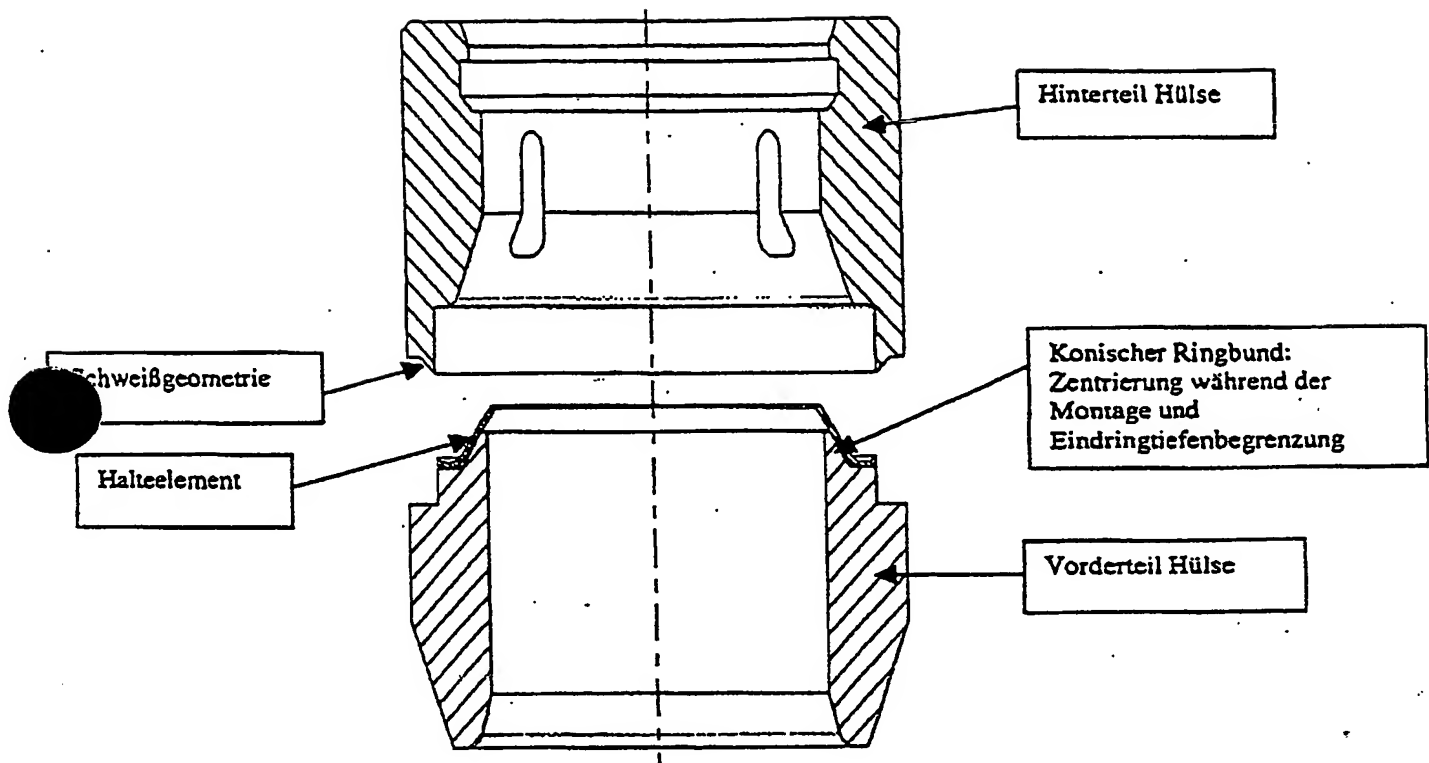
Ausführung der Hülse, ungeschweißt
